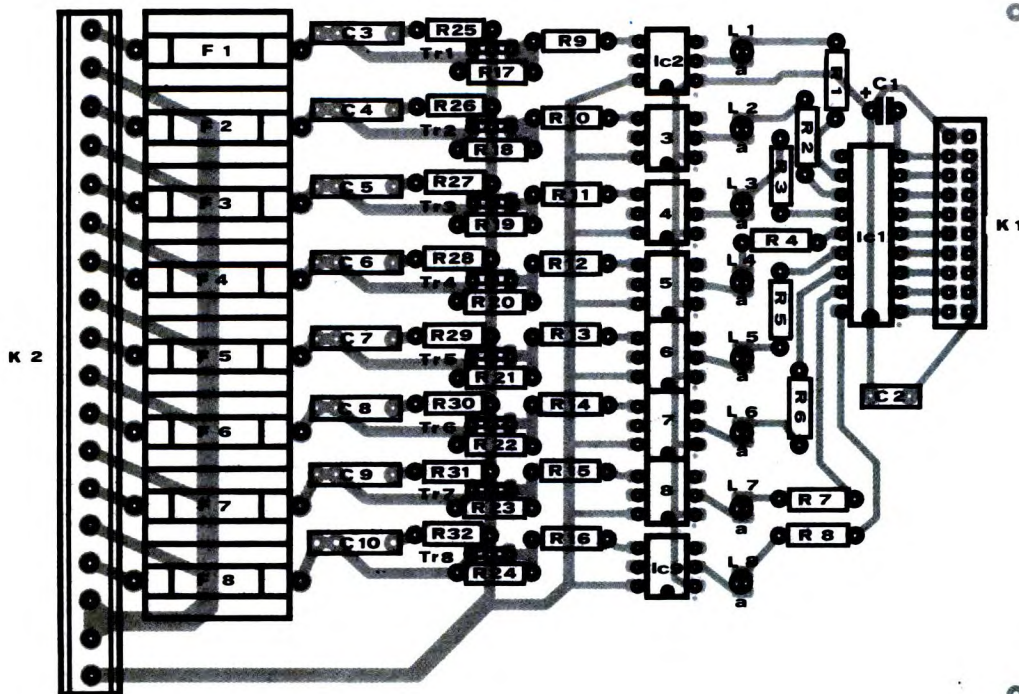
Disposizione dei componenti sulla bassetta dell'interfaccia di potenza.
